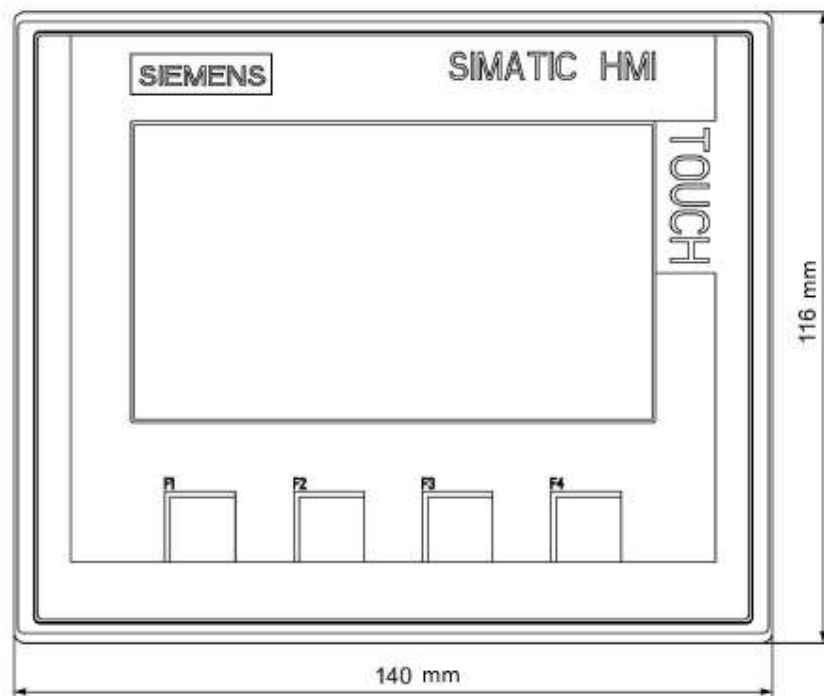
Dimensiones (mm) del Panel KTP400 Basic.
